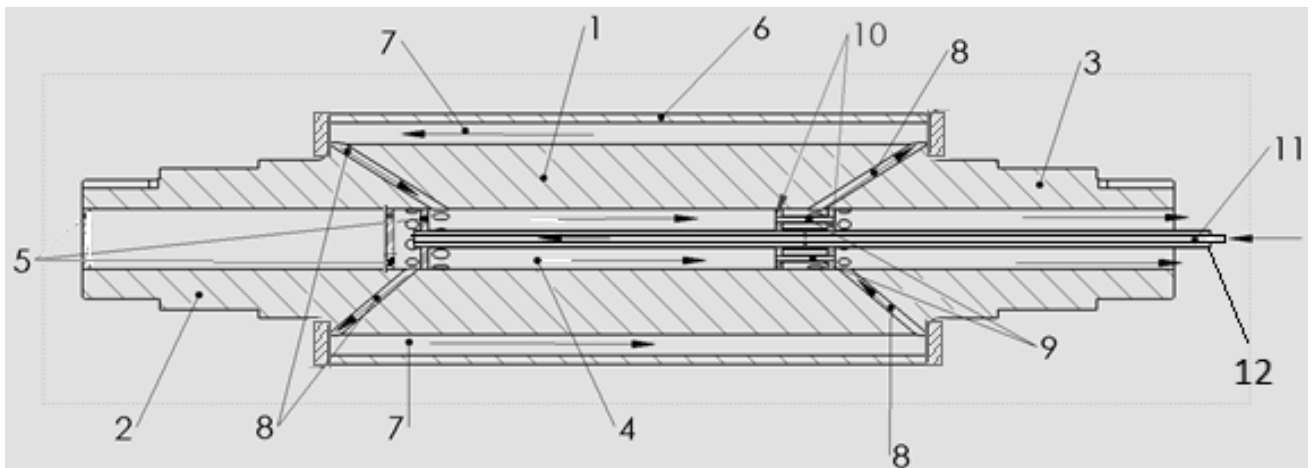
Загальний вид валка каландра в поздовжньому розрізі:
